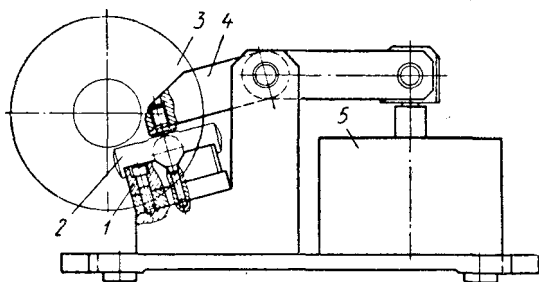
Приспособление для фрезерования торцов деталей типа крестовин
